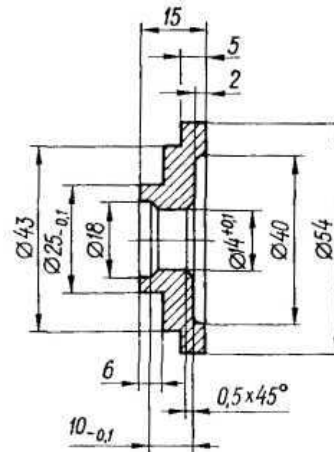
Оправка для запрессовки манжеты полуоси и поворотного кулака и выпрессовки внутренних подшипников колёсного редуктора
